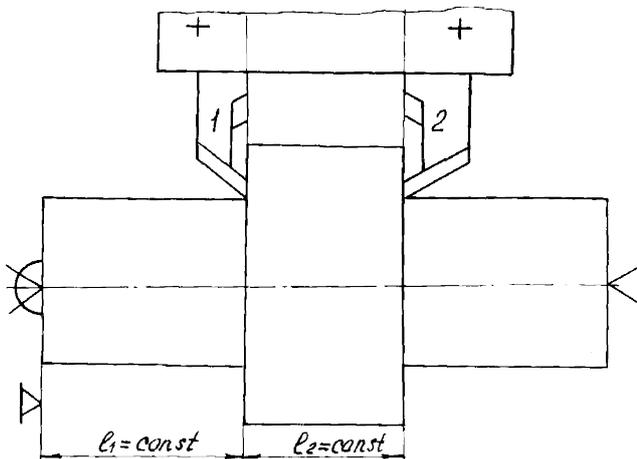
Схема обработки заготовки по методу автоматического получения размера
